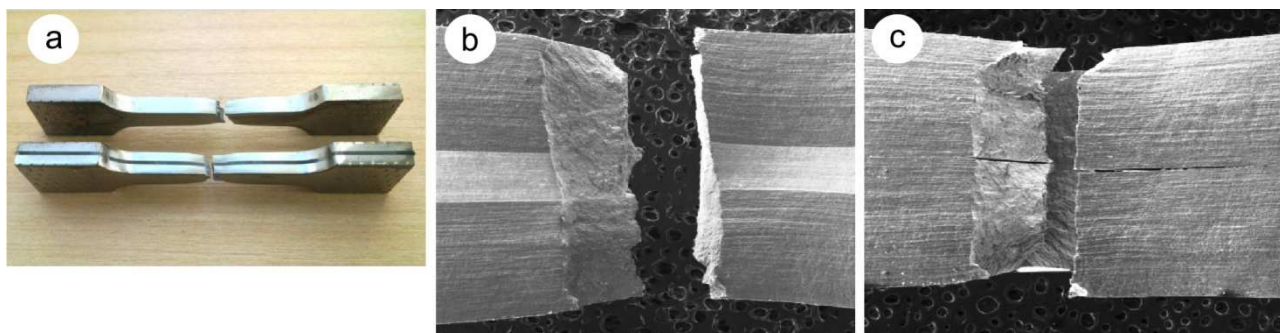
Внешний вид поверхности разрушенного образца, соединенных между собой листов, после испытания на растяжение вдоль сварного соединения:
